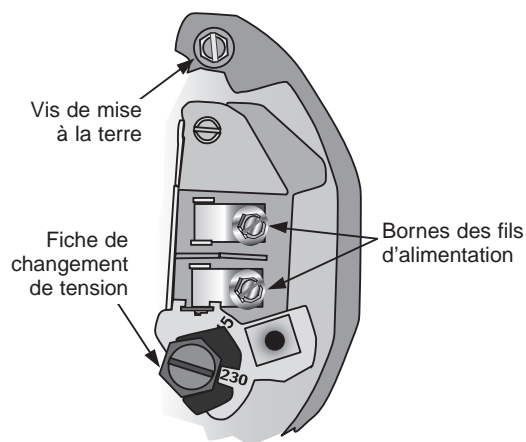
Tension réglée sur le courant de 230 volts. Sélecteur rotatif.
